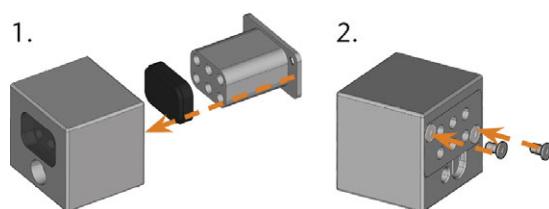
INSERIMENTO DI UN INSERTO IN UN MAGAZZINO UTENSILI
